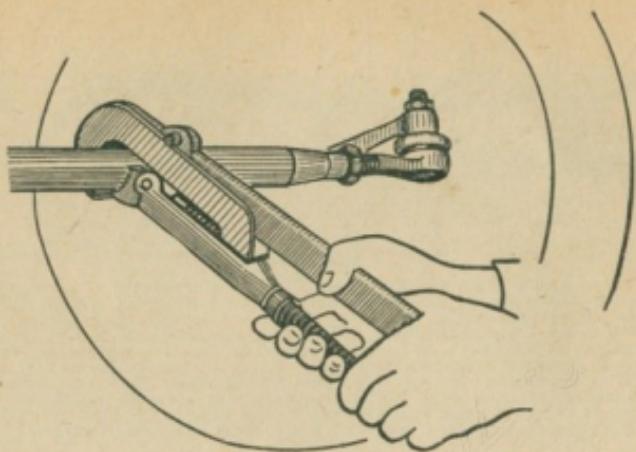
Регулировка схождения колес автомобиля УАЗ-469
